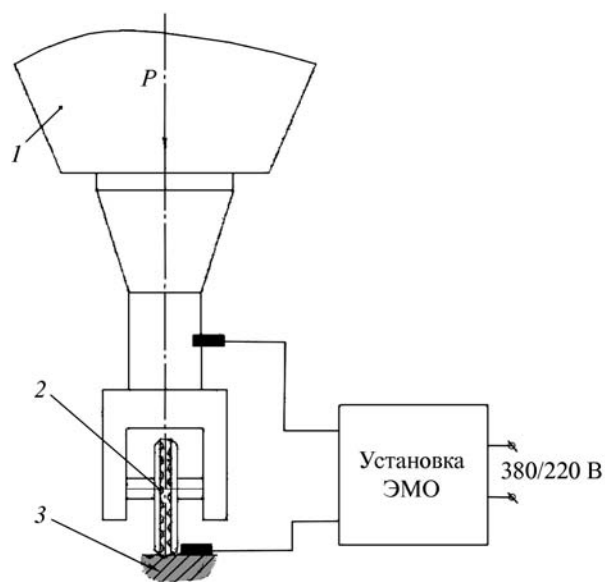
Схема процесса электромеханического упрочнения плоских поверхностей деталей:
